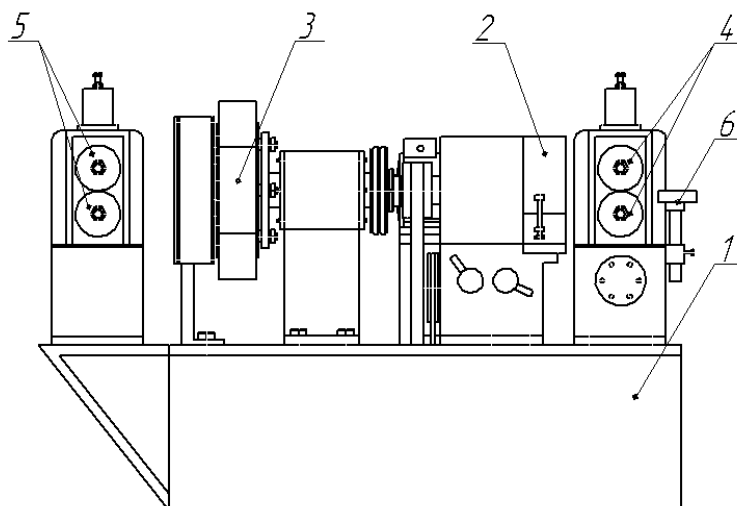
Общий вид круглопалочного станка КПА-50М:
